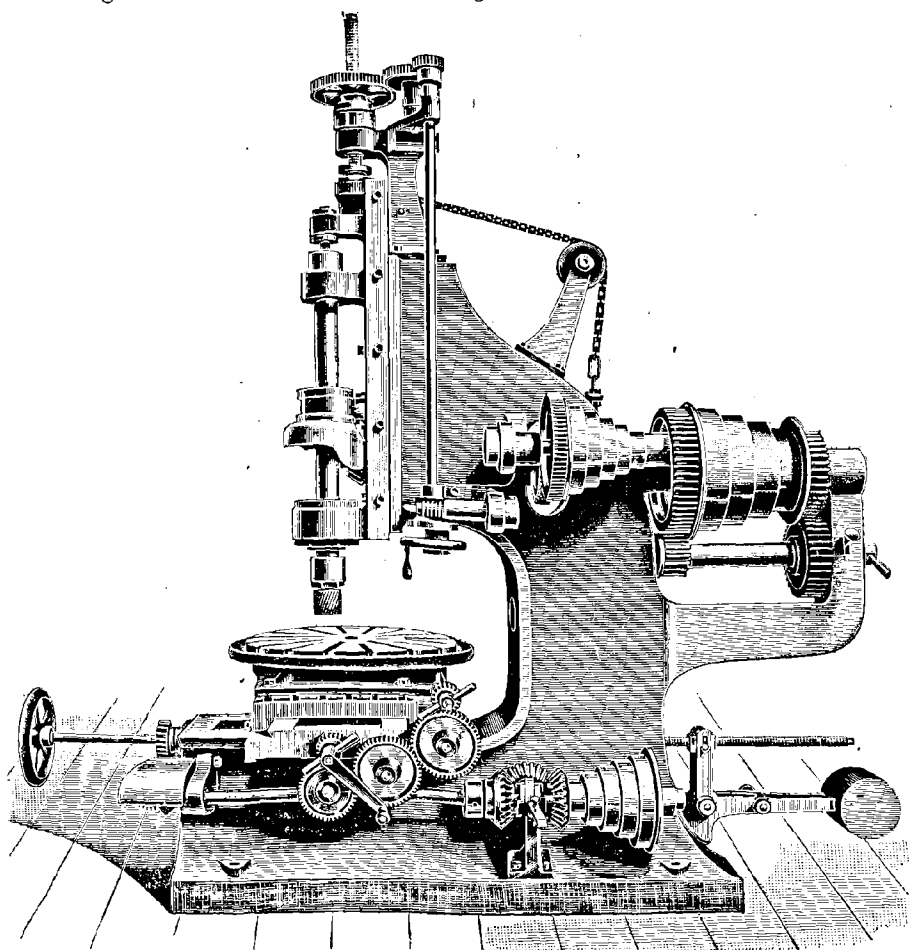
Machine à fraiser verticalement et à profiler L. Besse
